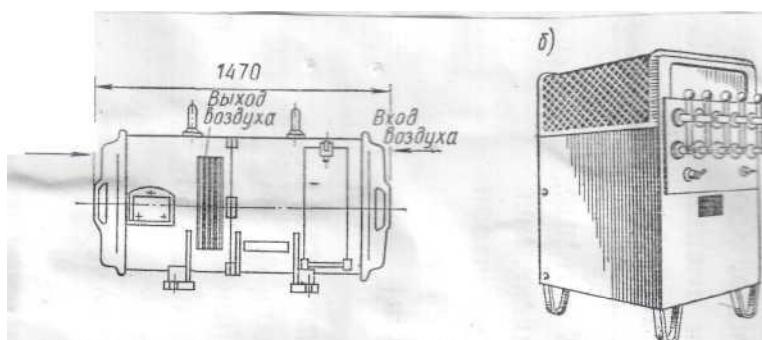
Сварочный преобразователь ПСМ-1000
